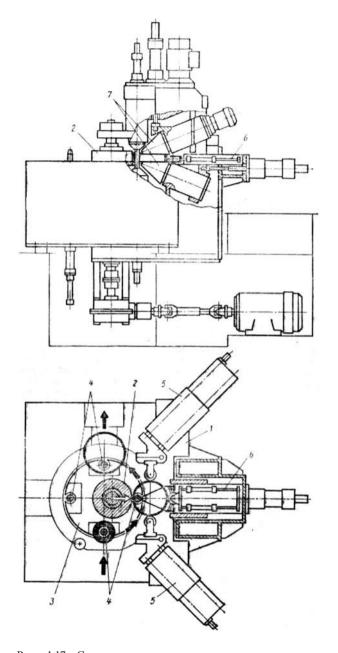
Схема радиально-осевого кольцераскатного стана типа RAW: I — станина; 2 — радиальный валок; 3 — приводной стол; 4 — холостые ролики; 5 — центрирующее устройство; 6 — измерительное устройство; 7 — осевые валки
